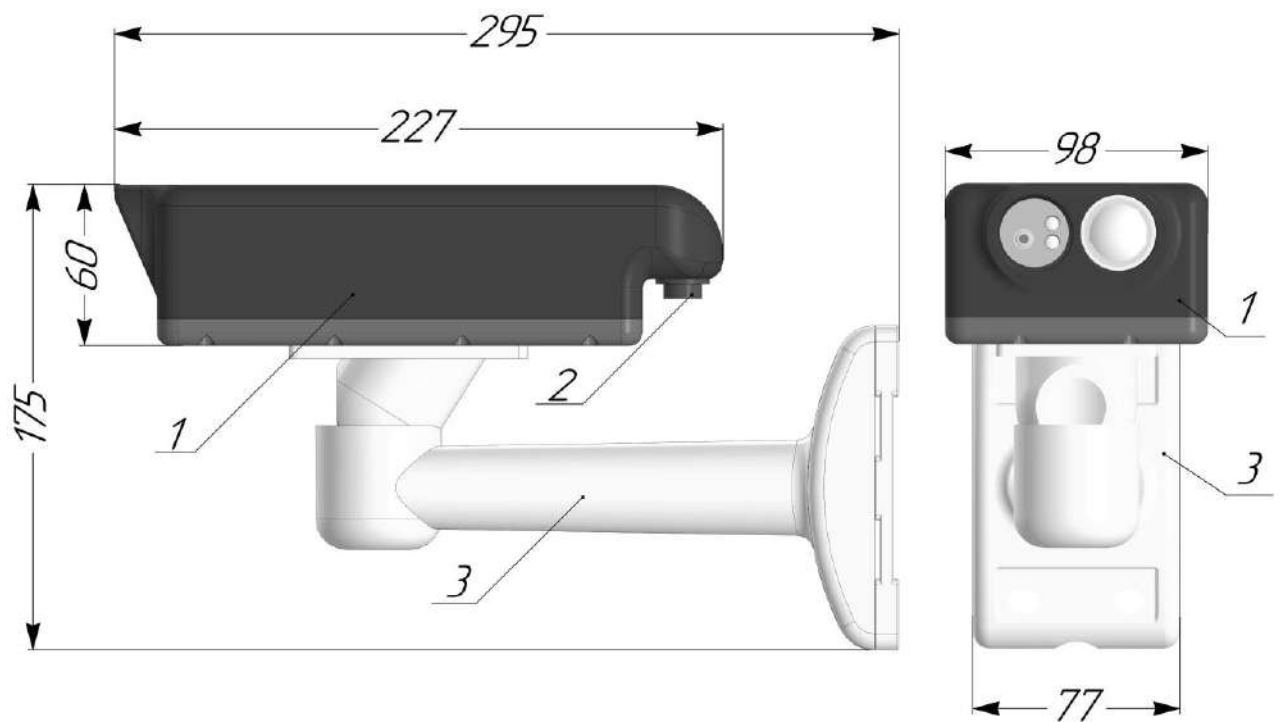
Внешний вид и габаритные размеры датчика ДСПД (1- Датчик, 2- разъем для подключения кабеля, 3 –кронштейн).
